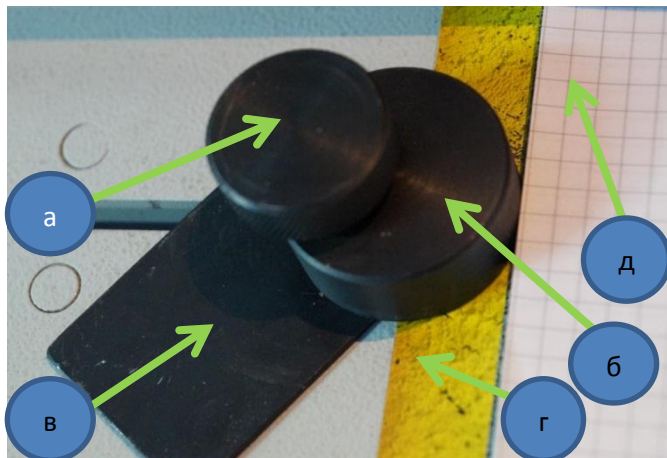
А – винт фиксатора упора Б- упор, В- промежуточный упор, Г- подложка Д- блок
